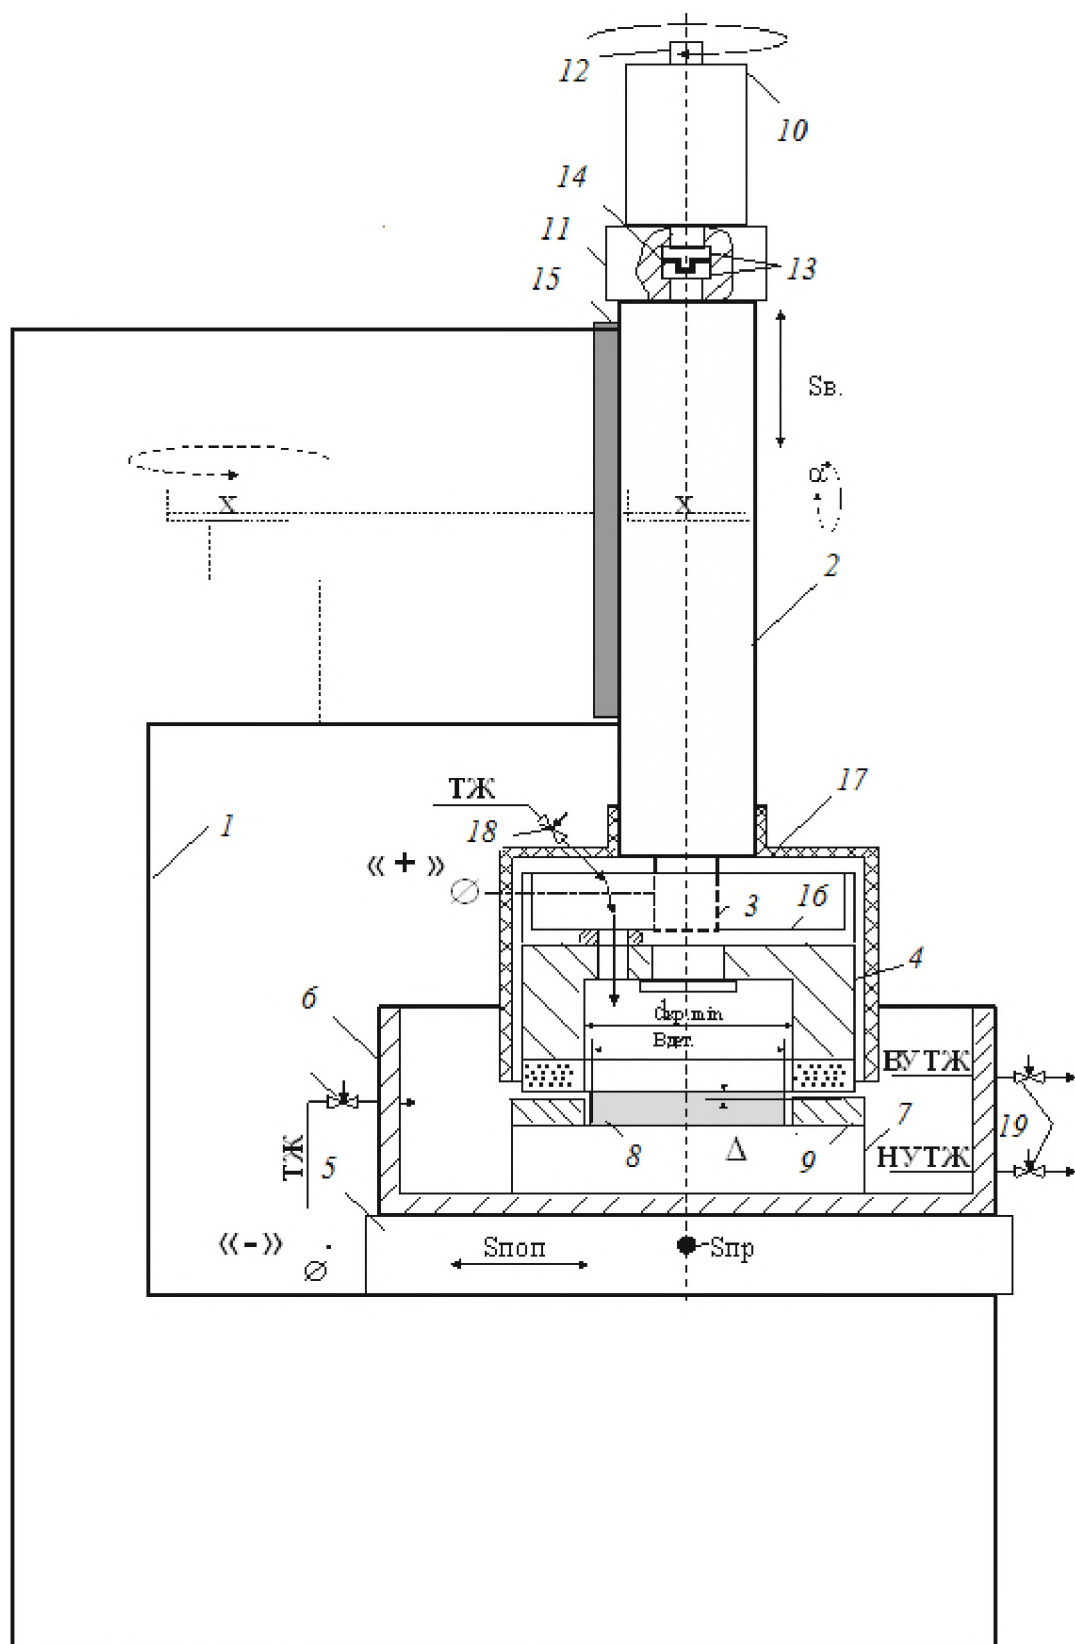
Конструкция плоскошлифовального станка с вертикальным расположением шпинделя
